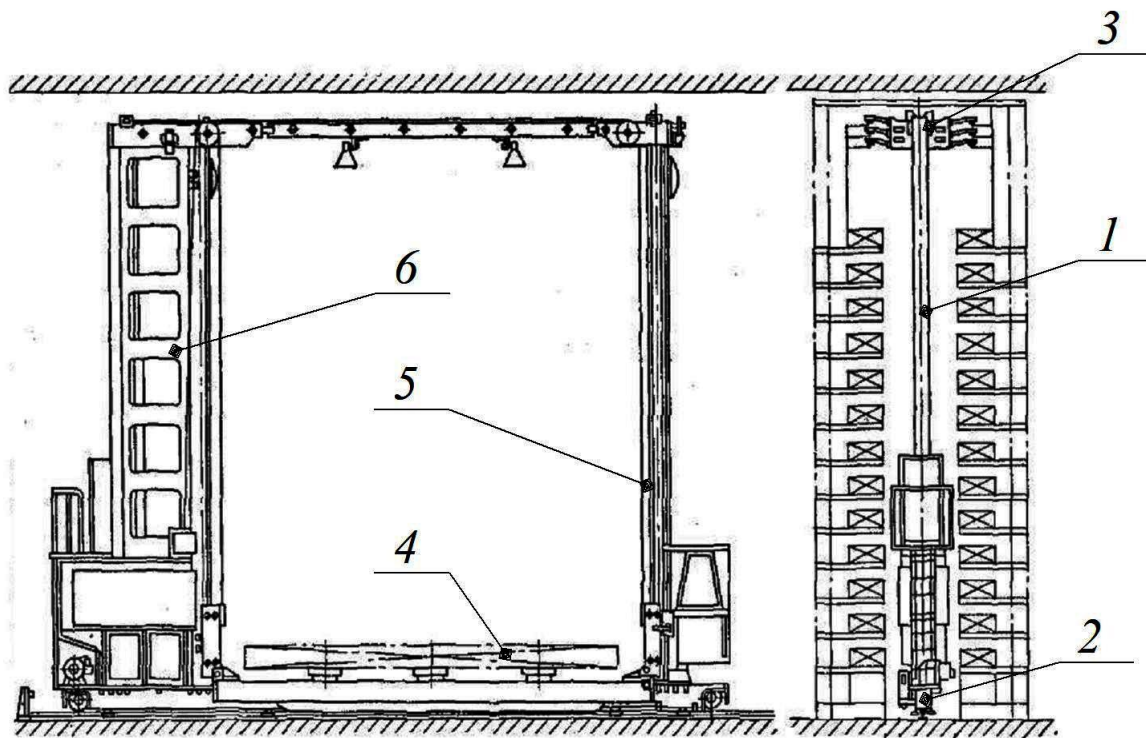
Стелажний двоколонний кран-штабелер, що спирається на підлогову рейку
